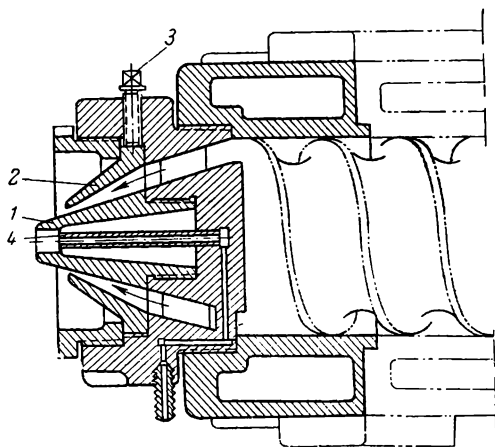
Головка червячного пресса (для выпуска камерного рукава):
